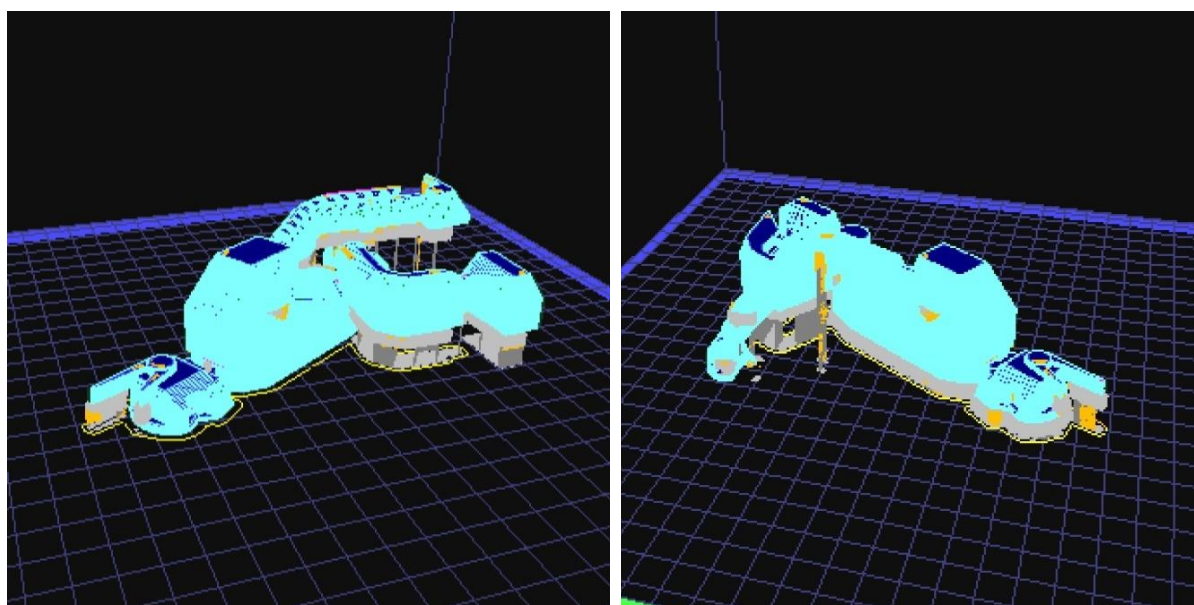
Zobrazení postavy robota na podložce a jeho základny.
